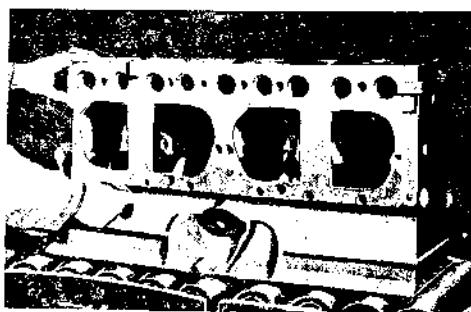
Контурный шаблон для проверки расположения отверстий на боковой поверхности блока.
